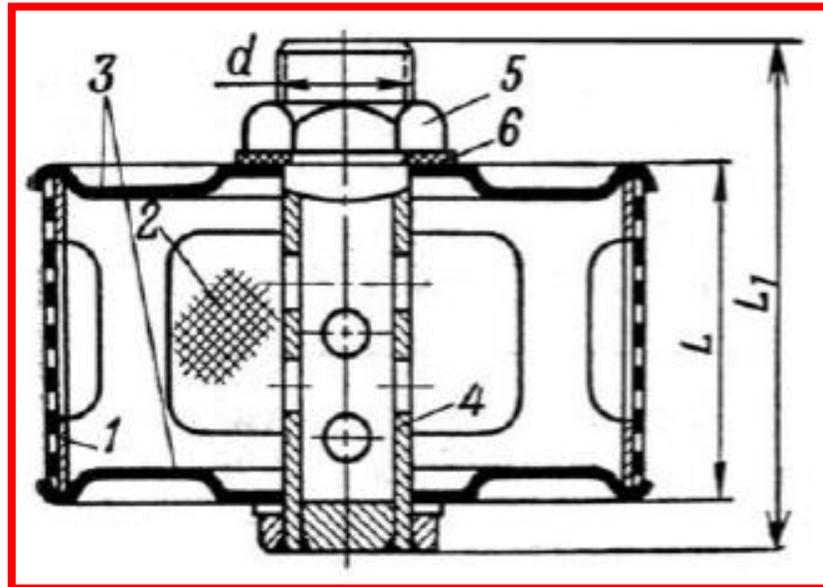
Сетчатый фильтр.1-корпус; 2-сетка; 3-диски; 4-перфорированная трубка;5-гайка; 6-прокладка.
